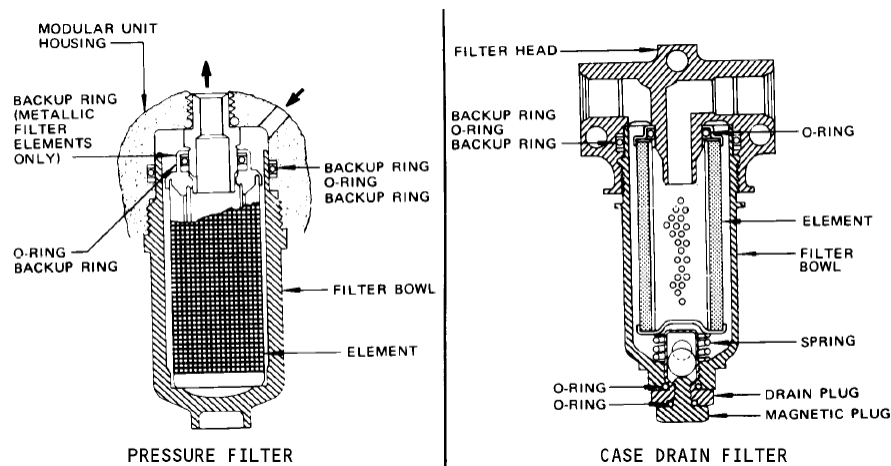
Filtros hidráulicos (hydraulic filters) (Fuente: B727-AMM)
